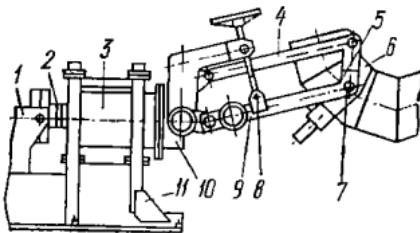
Установка УСО-1420 для сварки отводов:
